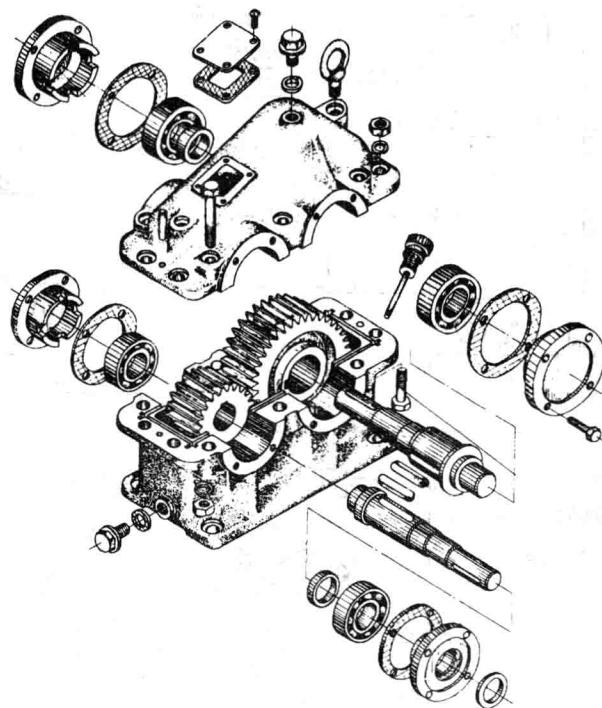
一级圆柱齿轮传动减速器结构组成展开图
